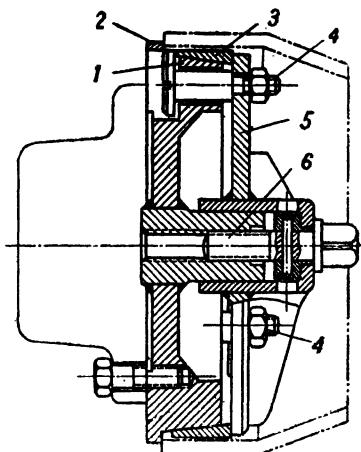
Сварная оправка для зажима крупных тонкостенных изделий.
